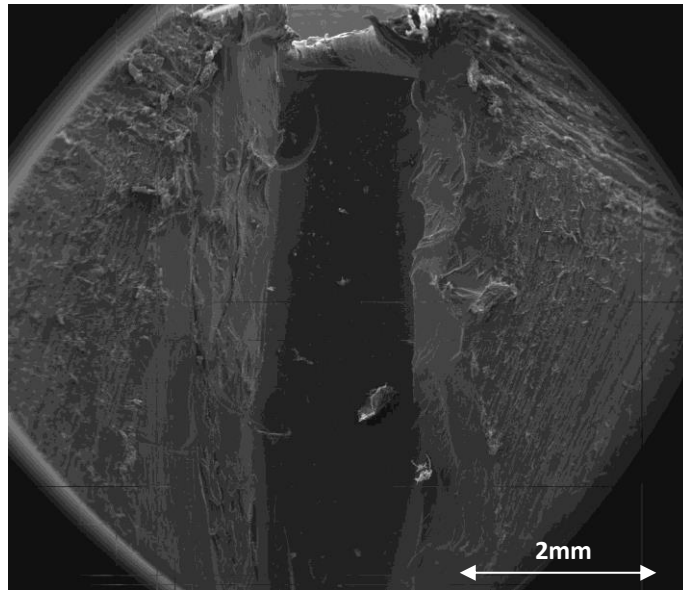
vista di un campione ricavato da un componente stampato con LIPSS parallele all'asse.
